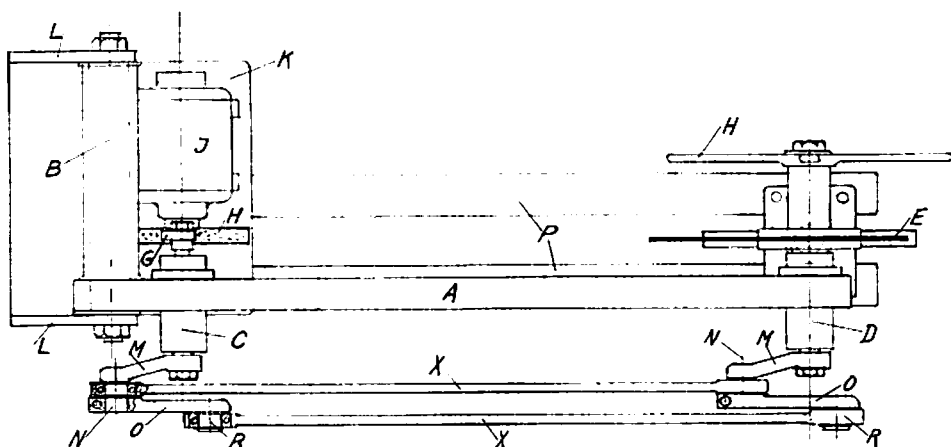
Draufsicht der 10:1-Schleifmaschine.
